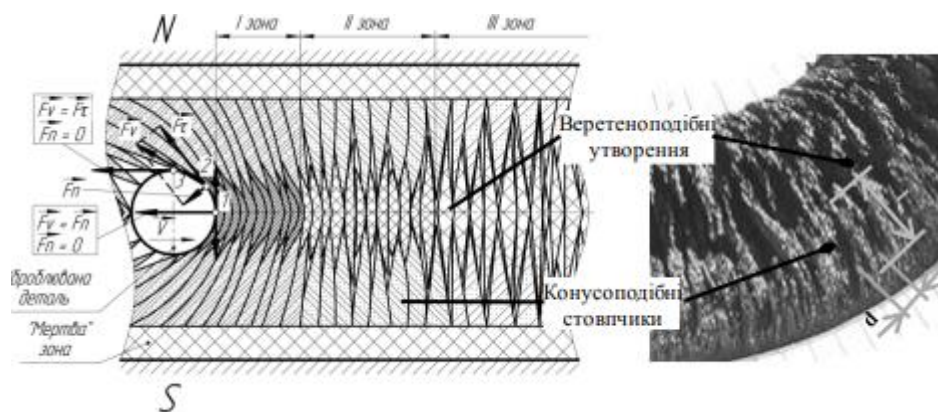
6 – Схема взаємодії структурних елементів МАІ з оброблюваними поверхнями деталі та зовнішній вигляд МАІ в робочому стані
